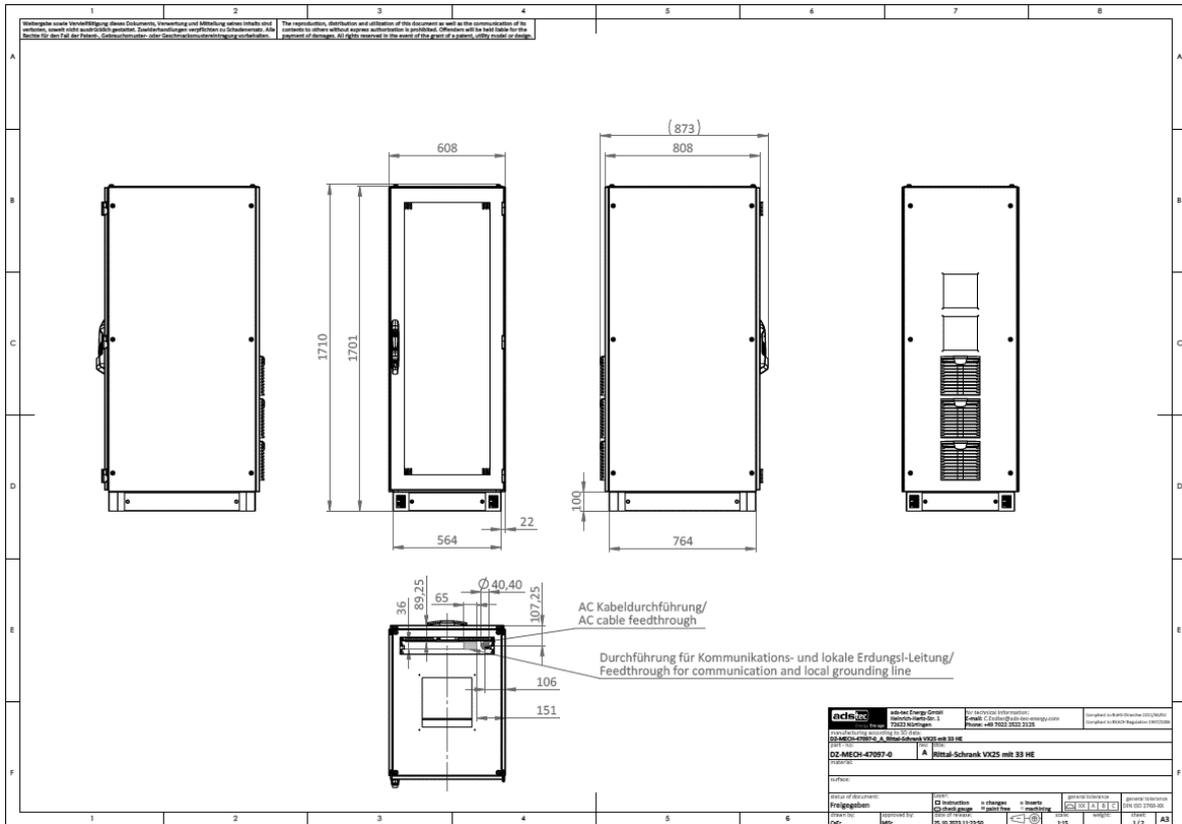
Konstruktionszeichnung Schrankgehäuse V1.0 - Blatt 1
